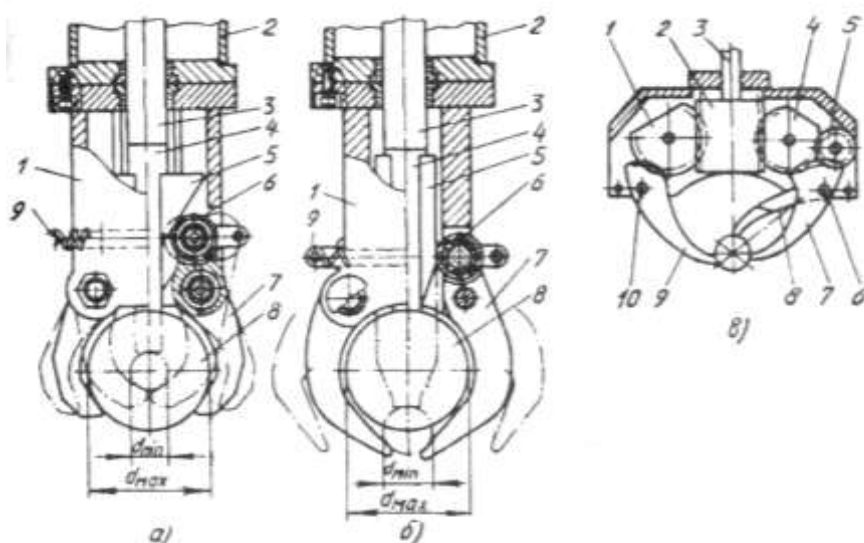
Центрирующее захватное устройство с тремя губками: а — для установки заготовок в центрах; б — для установки заготовок в призму; в — с губками специального профиля
